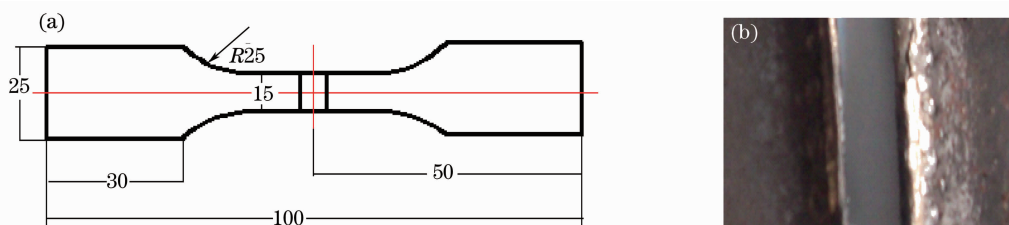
焊缝强度拉伸试验。(a) 拉伸试样;(b) 焊缝中部拉伸断样品
